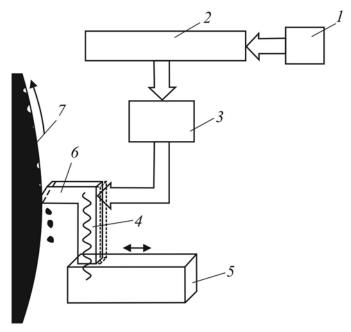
Схема работы режущей головки: $I-\text{RIP};\ 2-\text{контроллер};\ 3-\text{ЦАП};\ 4-$ электромагнит; 5- вибратор; 6- резец; 7- формный цилиндр
